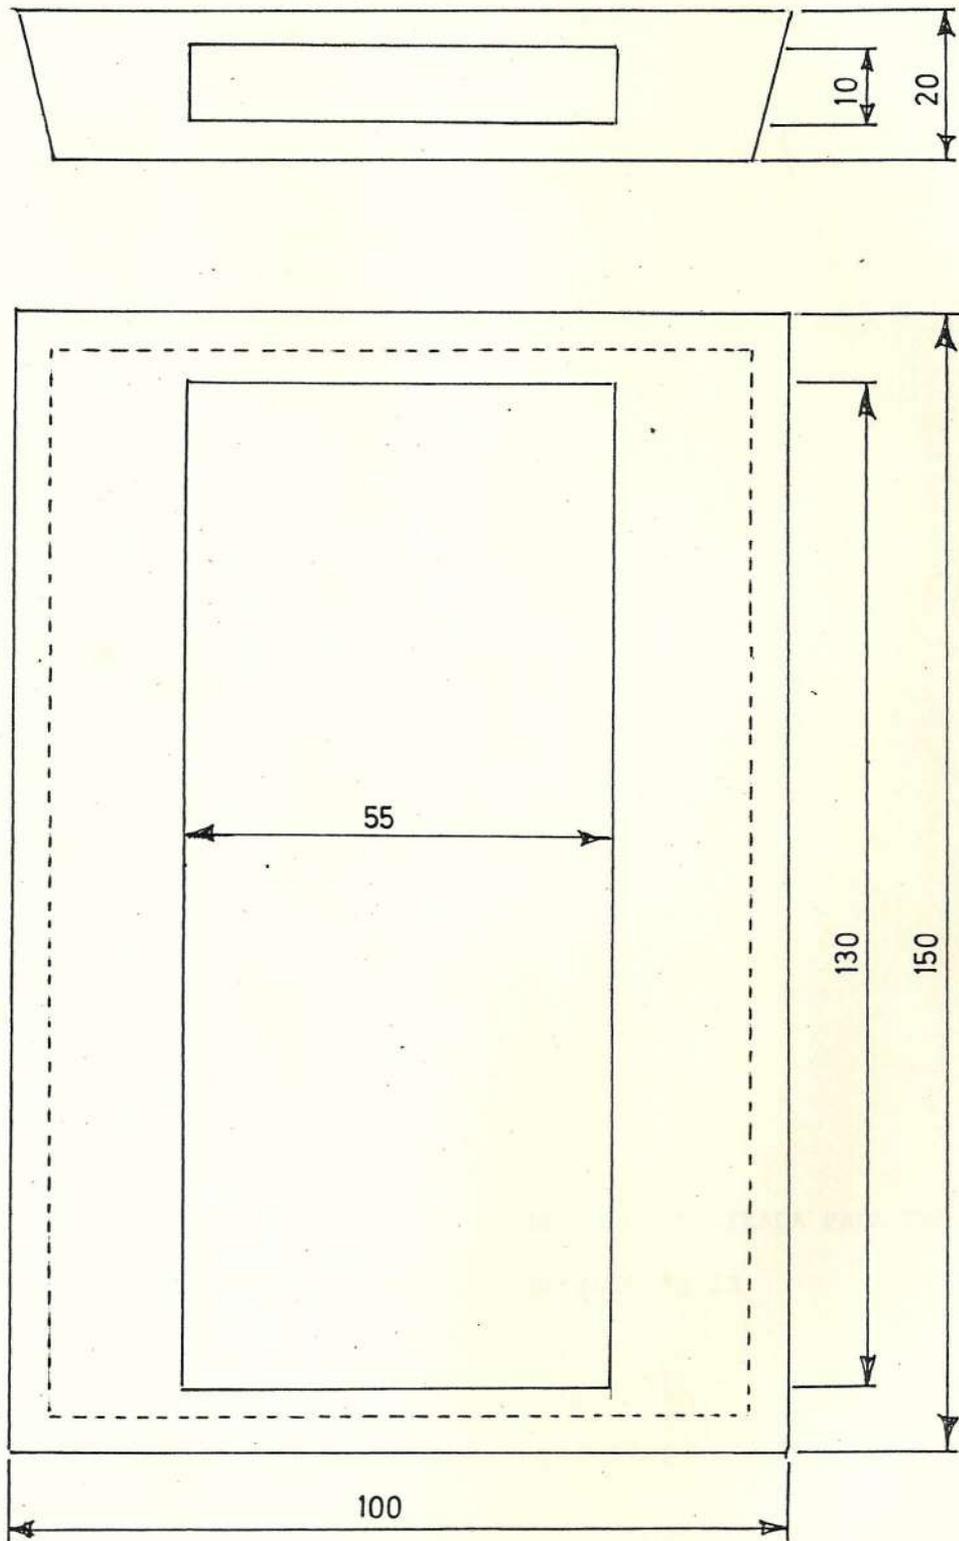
DIMENSIONES DE LINGOTE PARA OBTENER PROBETAS DEL ENSAYO DE IMPACTO.-
